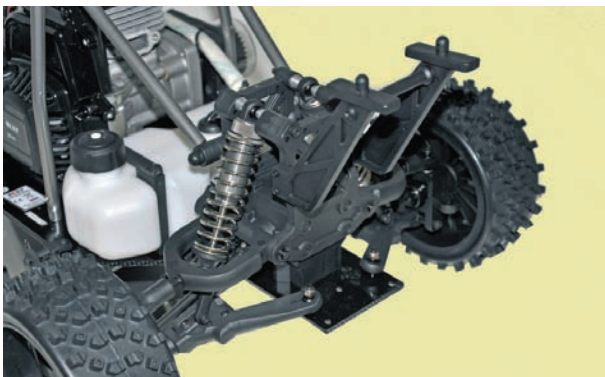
Bevor es an die Demontage der Dämpferbrücke geht, sind die Heckspoilerhalter abzuschrauben.
